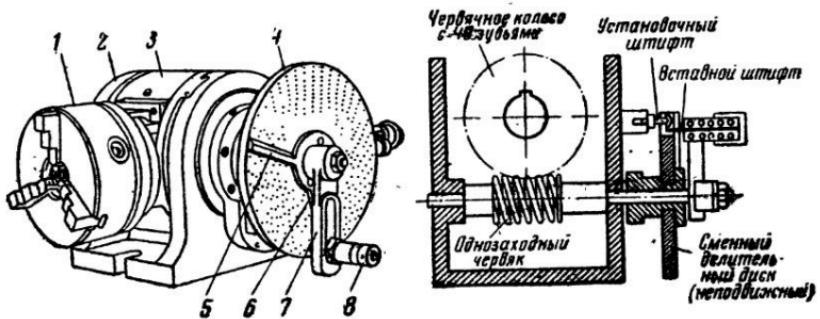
Делительная головка и ее устройство: 1 — самоцентрирующий патрон; 2 — корпус; 3 — колодка; 4 — сменный делительный диск; 5 — передняя линейка; 6 — задняя линейка; 7 — рычаг ручки; 8 — рукоятка с фиксатором.
